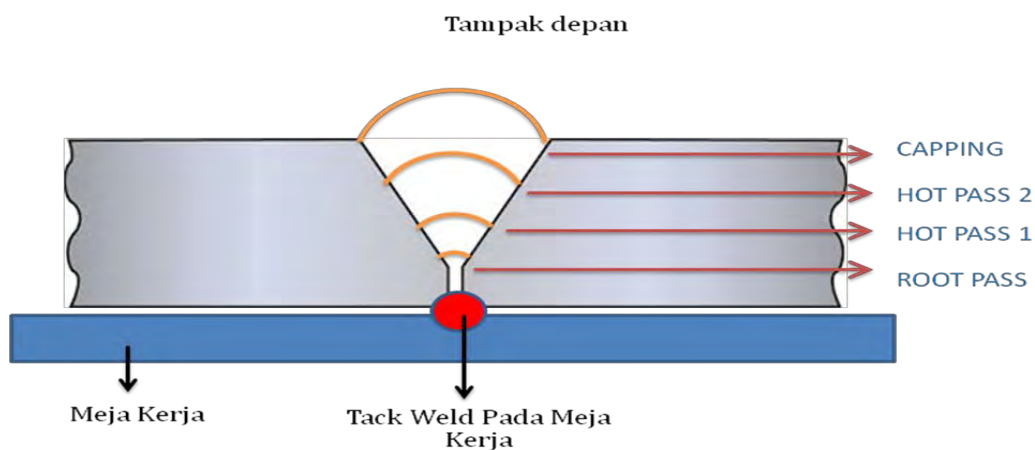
Tack Weld (sumber: dok.pribadi)
